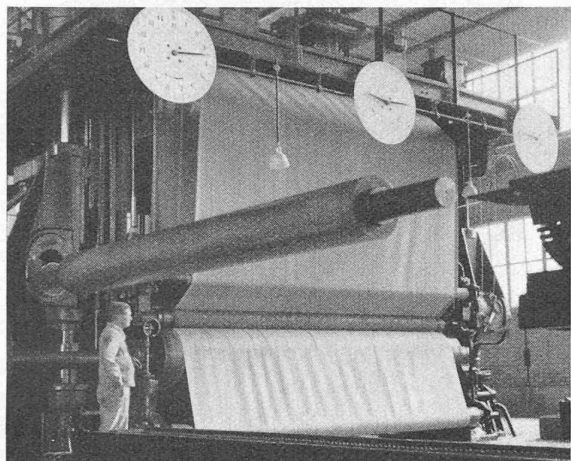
Machine pour la fabrication des tuyaux système Mazza.
